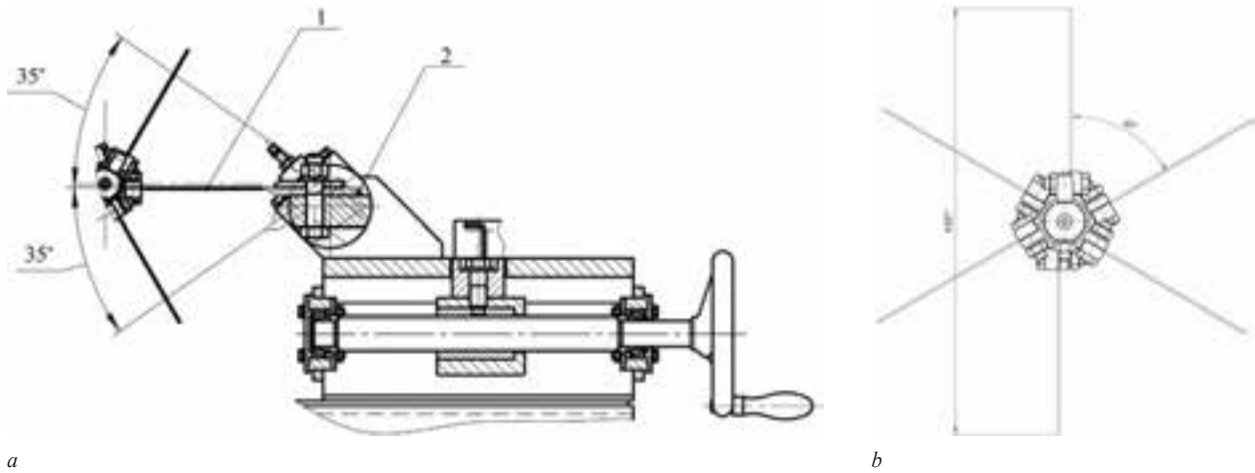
Схема установки образцов (а) и контробразцов (b) на стенде УИН: 1 — контробразец; 2 — образец-нож
